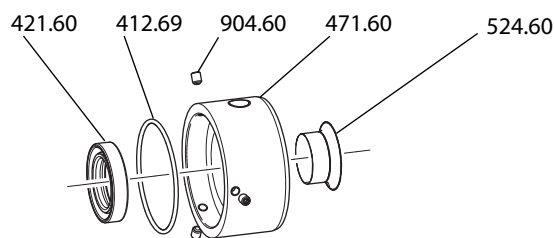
Caso d'applicazione B, premontare sull'albero (I) e premontare il corpo della pompa (II)
